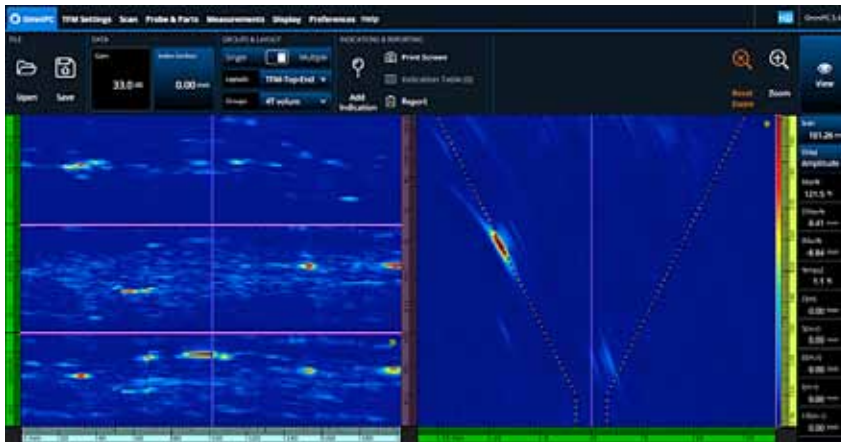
Inspección multigrupo de soldadura con tres modos distintos (TT, TT-TTT y TT-TT); a la izquierda se ven las tres vistas en planta (Top) y una transversal a la derecha.
